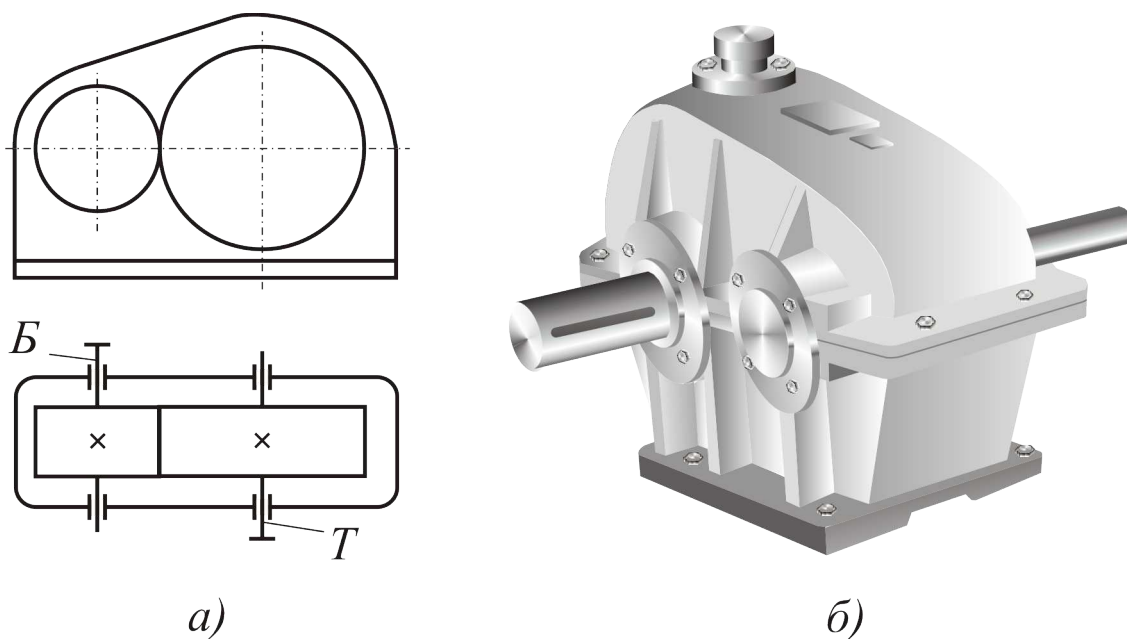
Одноступенчатый горизонтальный редуктор с цилиндрическими зубчатыми колёсами: а) кинематическая схема; б) общий вид
